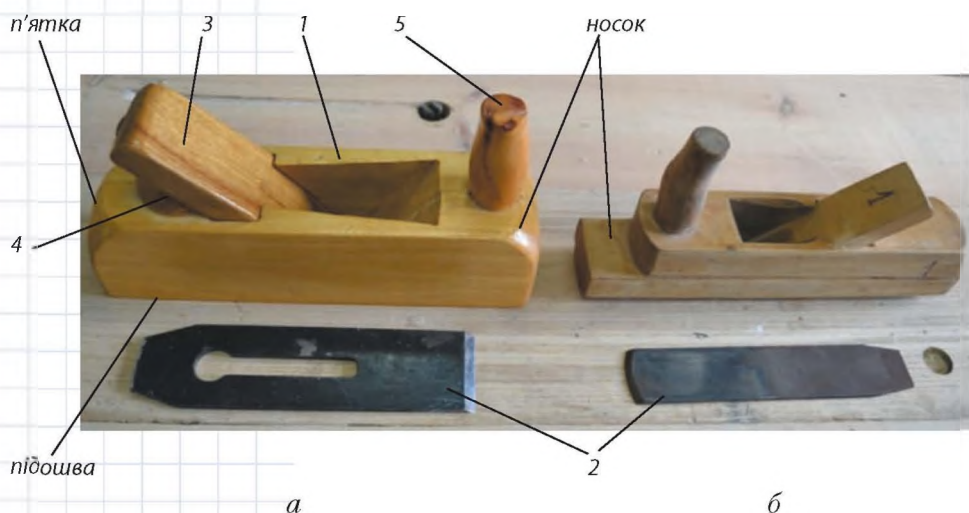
Будова рубанка (а) і шерхебеля (б)
